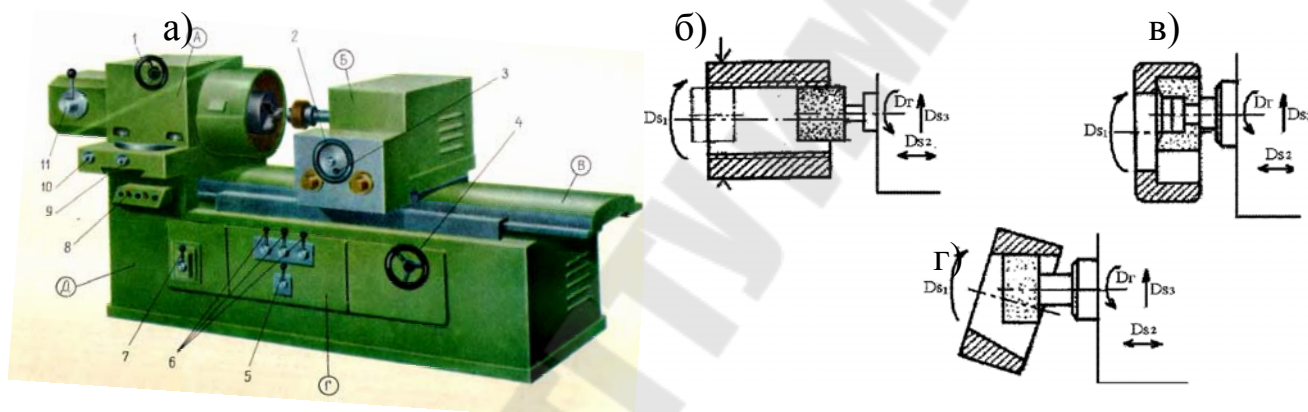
Общий вид внутришлифовального станка (а) и схемы шлифования отверстий (б - г)
